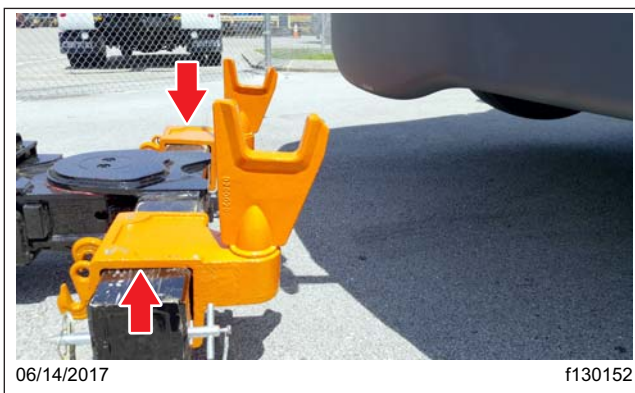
, Adaptadores de elevación instalados en la barra transversal
